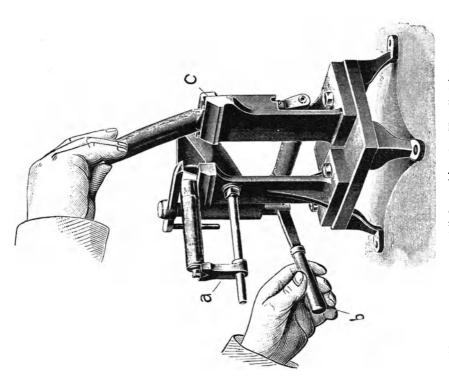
Tubenverschließmaschine für Handbetrieb.
